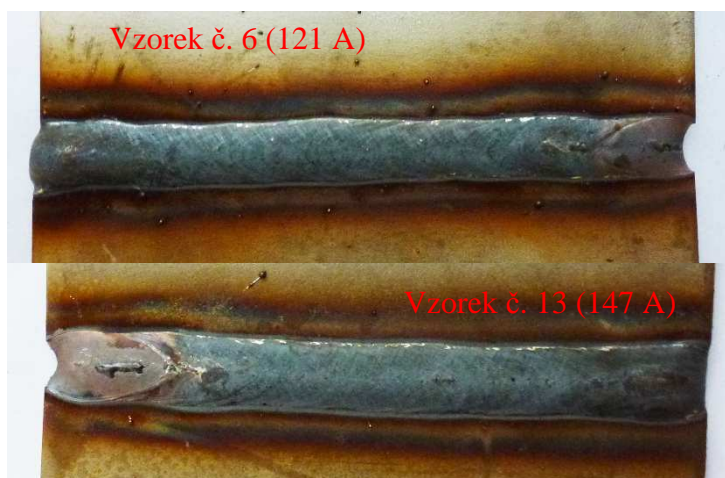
Příprava svarových spojů pro zkoušené vzorky [6]
